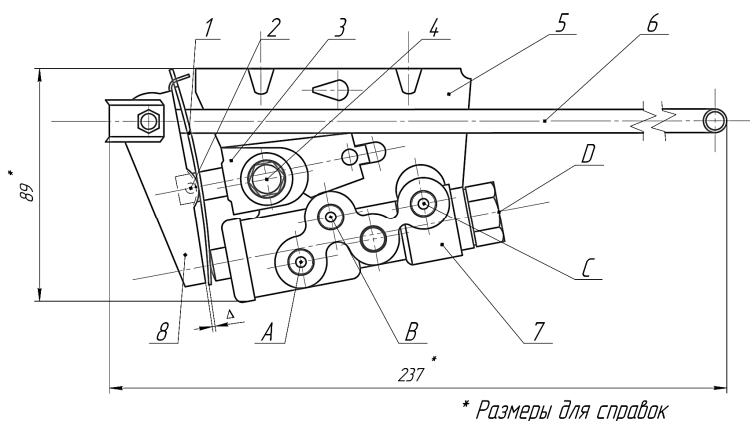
Регулятор тормозных сил с приводом: 1 – пружина рычага; 2 – штифты; 3 – двуплечий кронштейн рычага привода РТС; 4 – крепление привода; 5 – кронштейн крепления регулятора к кузову автомобиля; 6 – упругий рычаг (торсион) привода РТС; 7 – РТС; 8 – рычаг привода регулятора; A, D – входные отверстия РТС; B, C – выходные отверстия РТС
